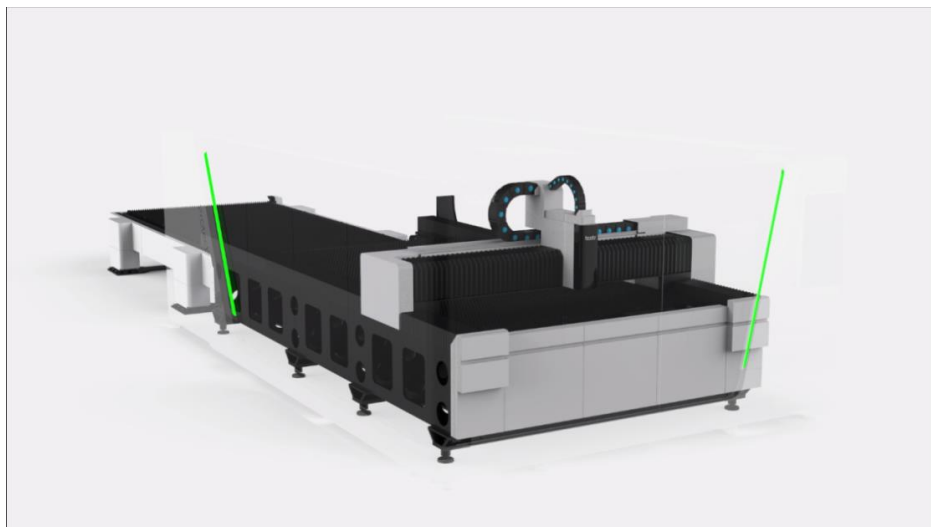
Оптоволоконный станок для лазерной резки BODOR модель S4020 (вид изнутри)
